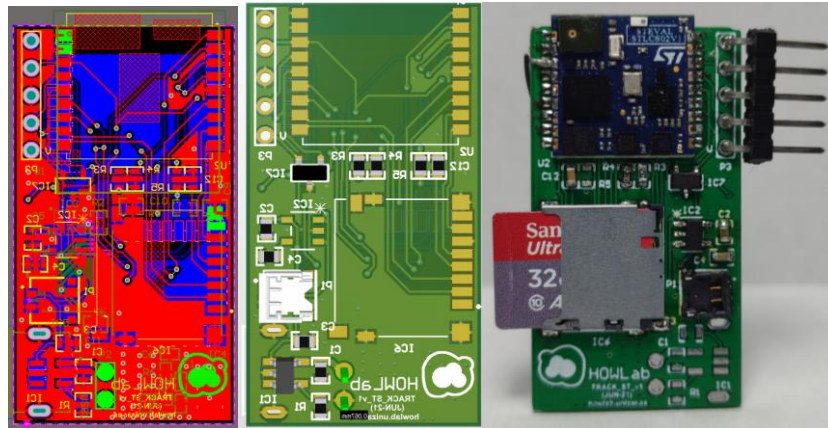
Dos Imagen de la PCB vistas desde Altium (imágenes de la izquierda) y PCB ya soldada.
